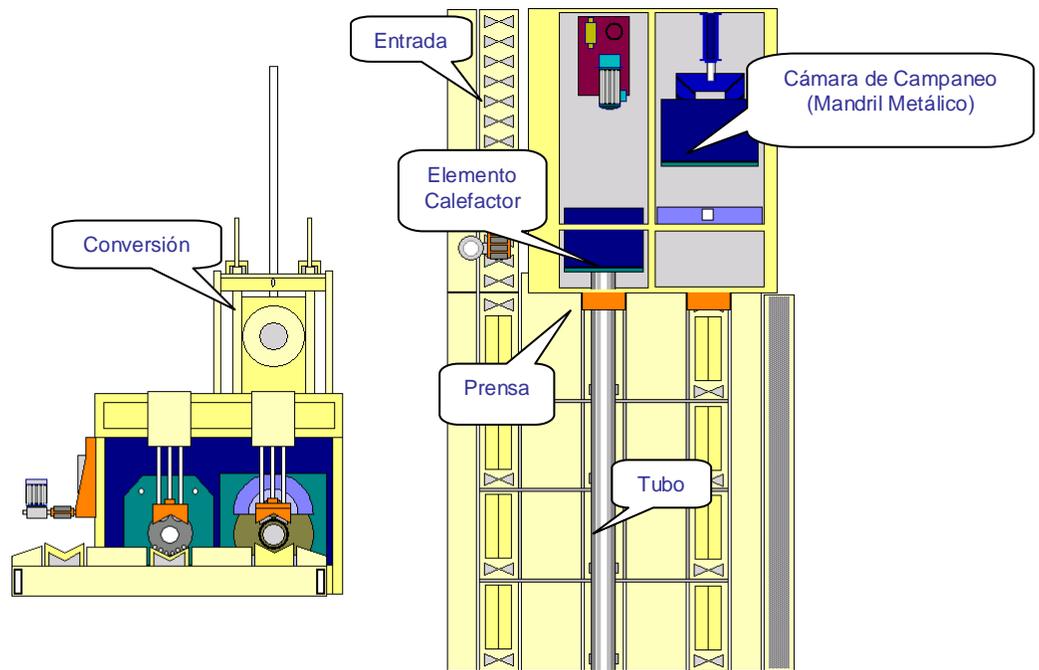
Vista frontal y superior de una Máquina Campaneadora IPM 500.
